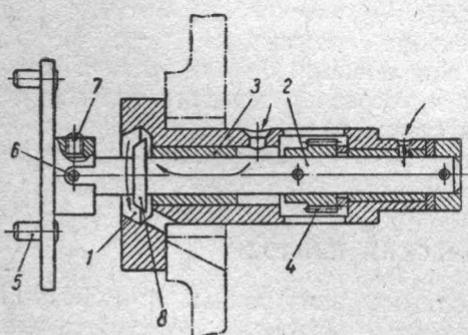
Ведущий вал в разрезе: 1 — подшипник; 2 — вал; 3 — втулки; 4 — шестерня; 5 — фланец; 6 — штифт; 7 — стопор; 8 — разбрызгивающее кольцо
